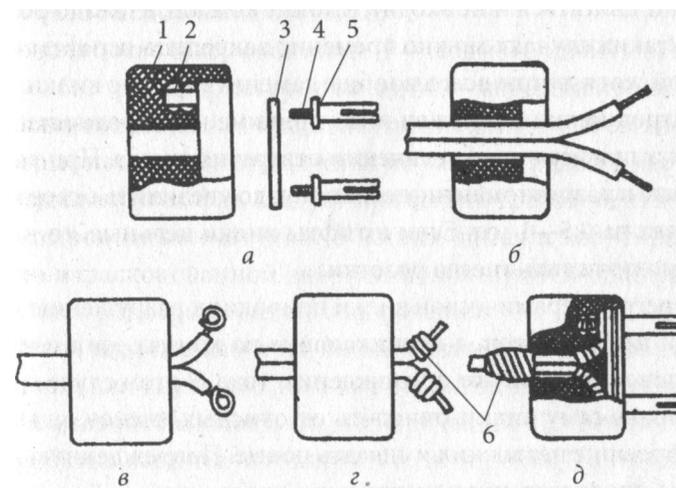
Монтаж и ремонт вилки с разрезными штифтами и цельным пластмассовым корпусом: *а* — разборка вилки; *б* — протягивание проводников и зачистка жил по длине 10—15 мм; *в* — загиб концов жил в петли; *г* — изоляция места закручивания жилы, образующей петлю; *д* — наложение на петли планки и закручивание штифтов в спецгайки: 1 — корпус; 2 — спецгайка; 3 — планка; 4 — разрезной штифт; 5 — гайка шестигранная; 6 — изоляционная лента
